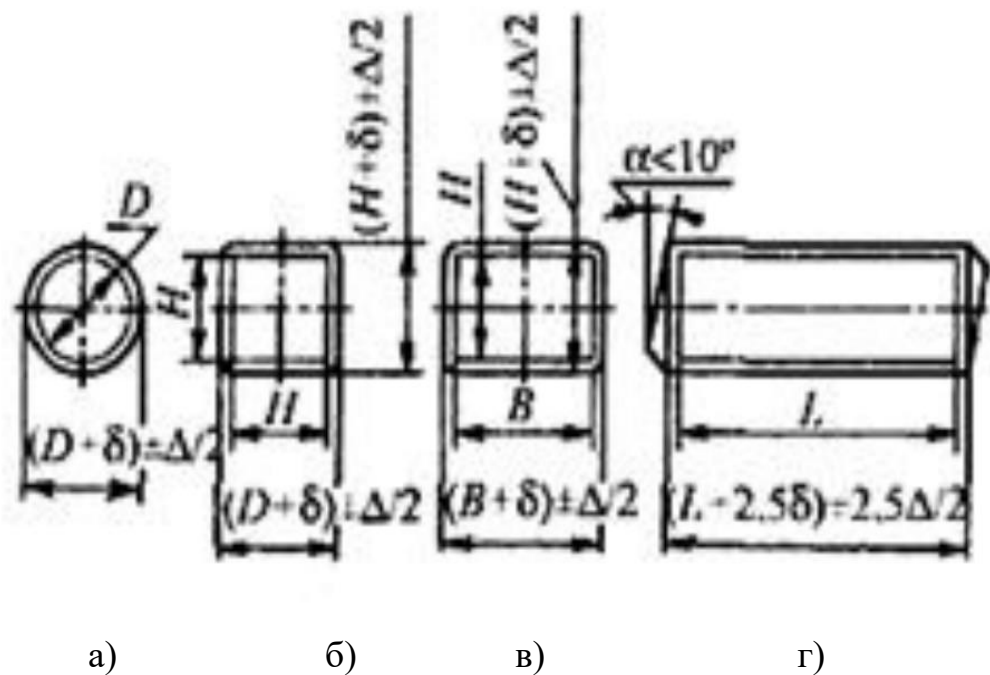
Схема призначення припусків і допустимих відхилень розмірів заготовок-поковок для деталей однієї довжини L (г) і різних форм перерізу: а – циліндричної; б – квадратної; в - прямокутної
